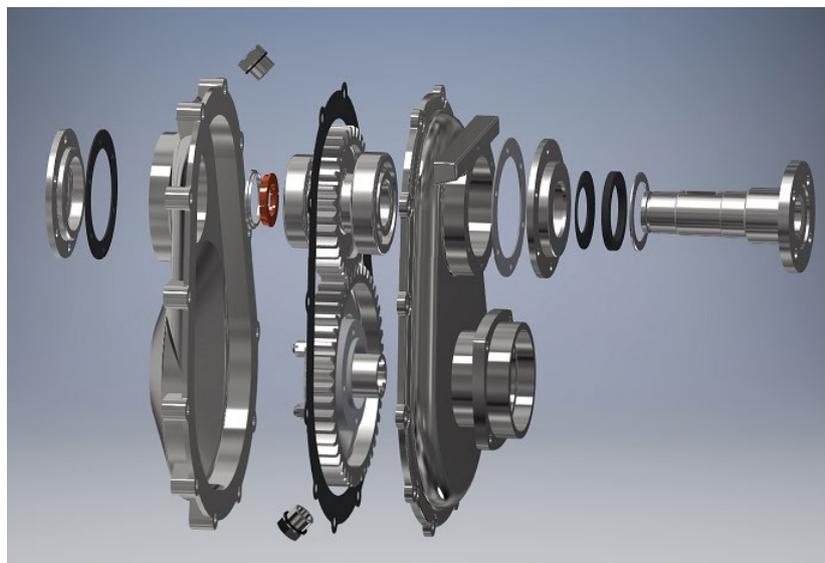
Разнесенная сборка редуктора привода лебедки
